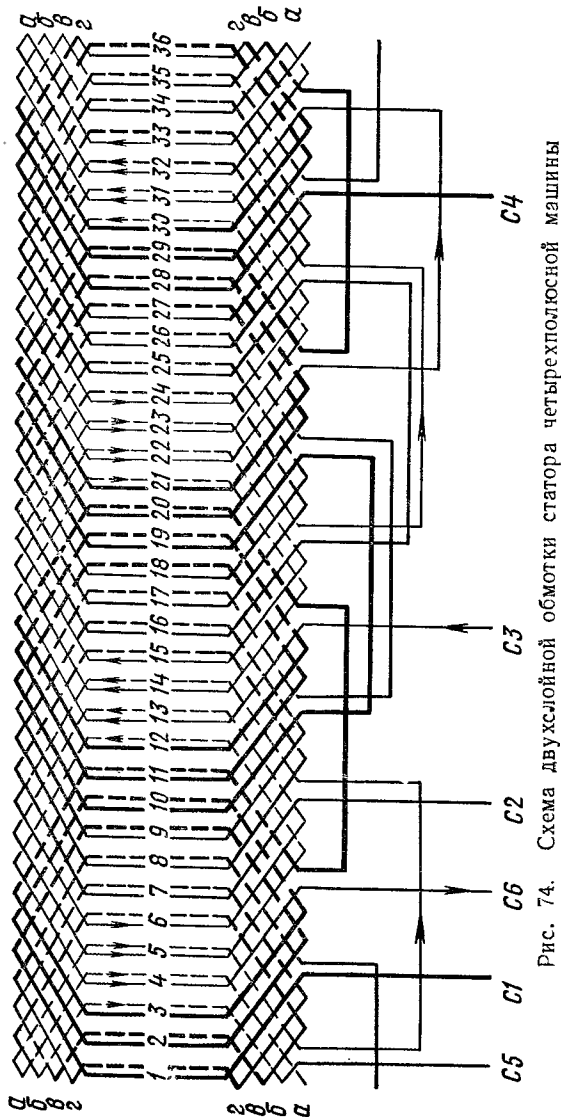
Схема двухслойной обмотки статора четырехполюсной машины
